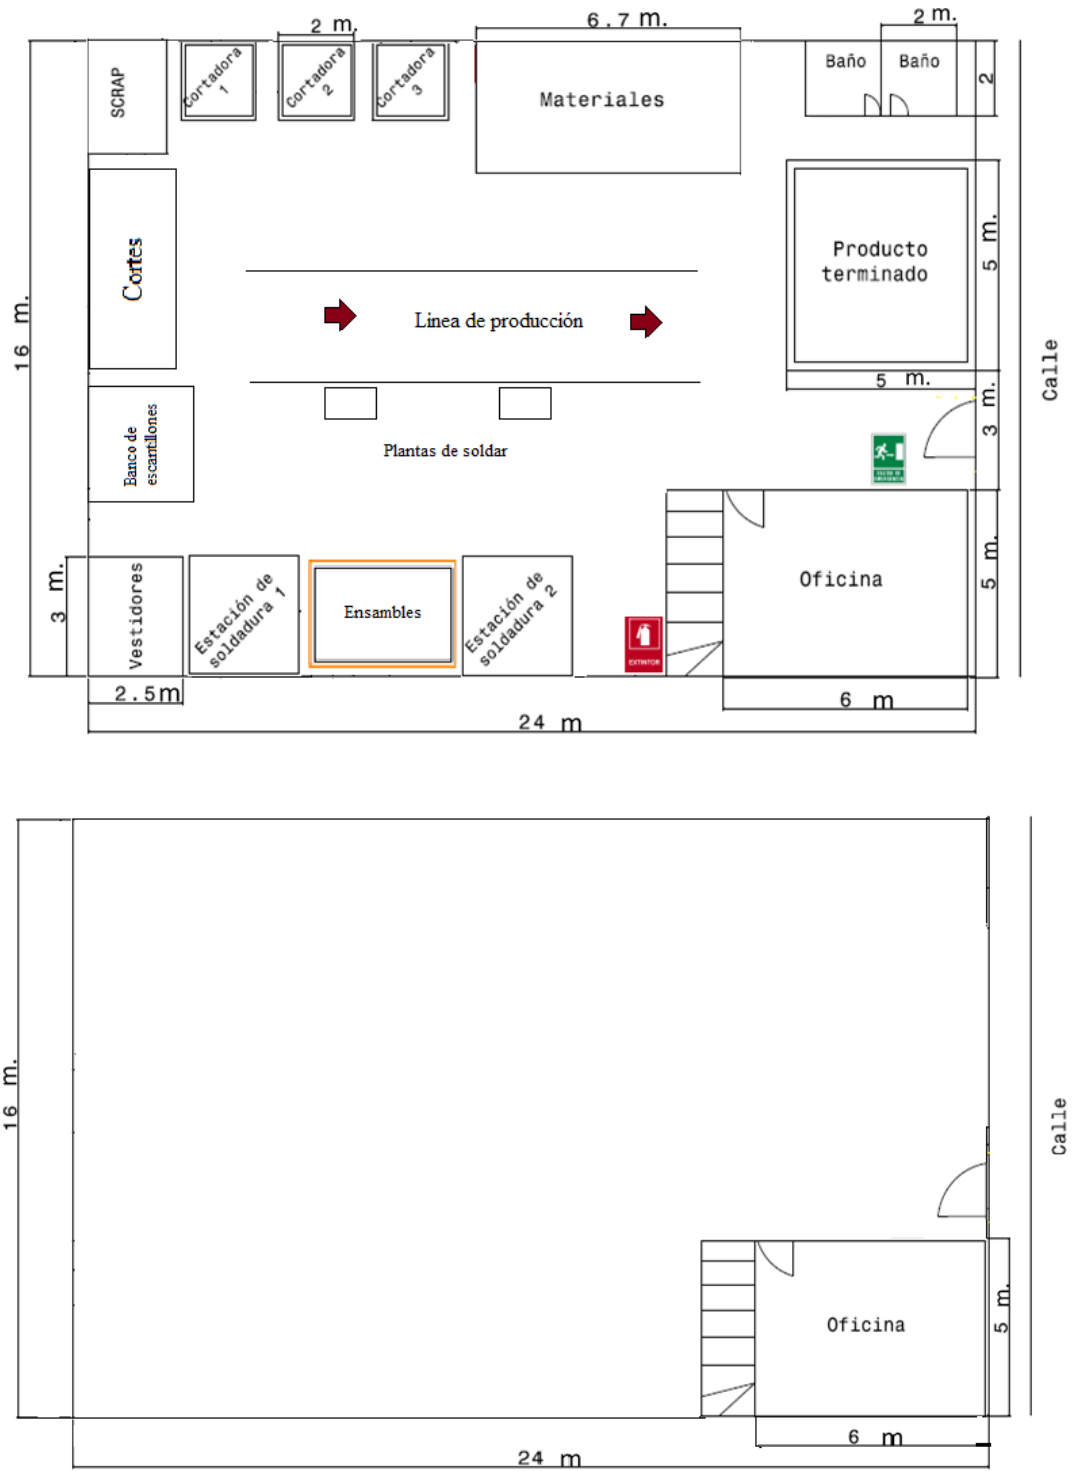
Segunda propuesta de Layout planta baja y alta
